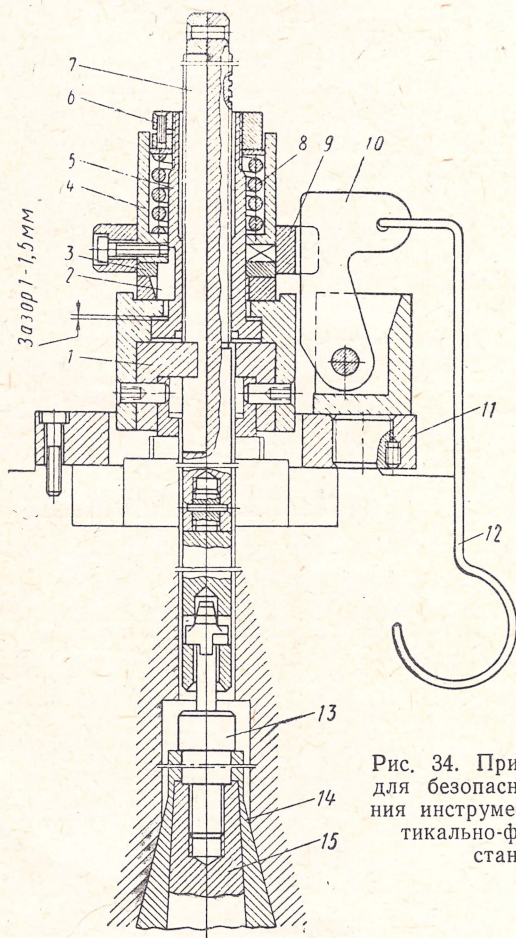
Приспособление для безопасного крепления инструмента на вертикально-фрезерном станке
